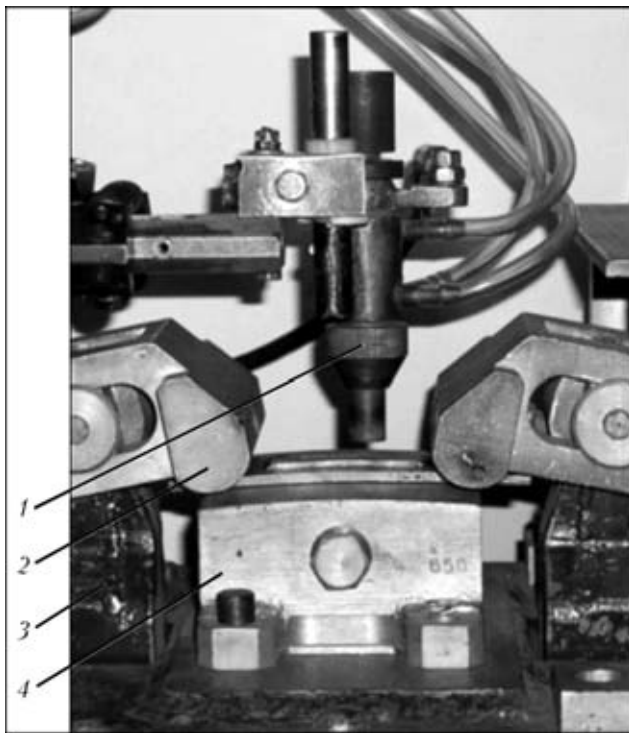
Внешний вид рабочего угла установки и составного образца (оправки для изгиба радиусом 650 мм): 1 — горелка ТИГ; 2 — зажим; 3 — образец; 4 — оправка
